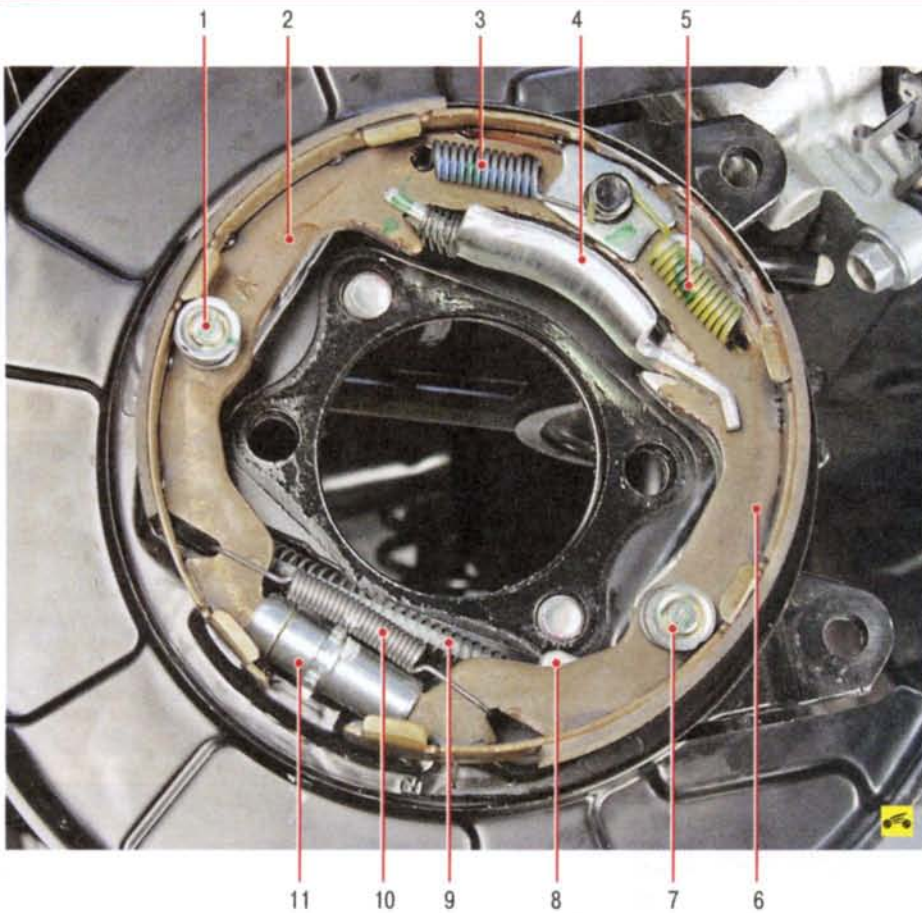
Детали стояночного тормозного механизма: 1, 7 – опорные стойки колодок; 2 – передняя колодка стояночного тормоза; 3 – верхняя стяжная пружина передней колодки; 4 – разжимная планка; 5 – верхняя стяжная пружина задней колодки; 6 – задняя колодка стояночного тормоза; 8 – разжимной рычаг привода колодок; 9 – задний трос стояночного тормоза; 10 – нижняя стяжная пружина колодок; 11 – регулировочное устройство тормозных колодок стояночного тормоза
